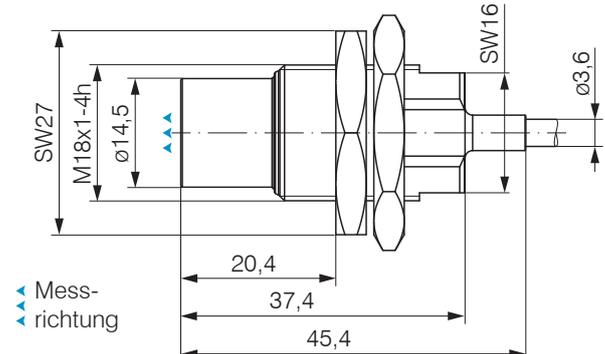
Maßzeichnung Sensoren ES-U6-C-CAx/mB0
